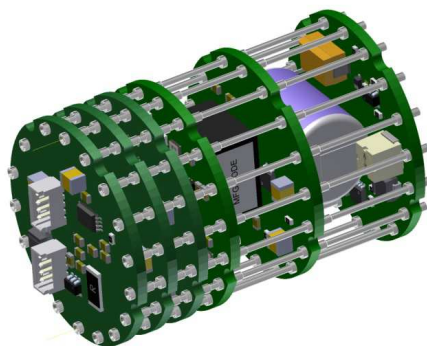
Zmontowana płytki testowa do badań zasadniczych elementów laserowego sensora zbliżeniowego.
